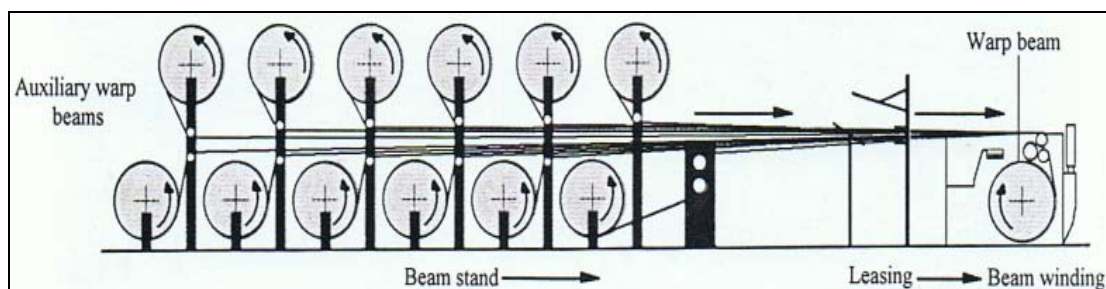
เครื่องเตรียมเส้นด้ายยืน Warping Machine
